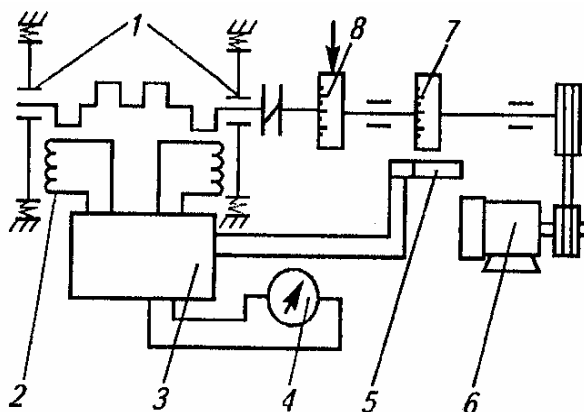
Схема станка для динамической балансировки деталей: 1 – опоры (люльки); 2 – датчик перемещений; 3 – блок усиления; 4 – миллиамперметр; 5 – лампа стробоскопа; 6 – электродвигатель; 7 – лимб стробоскопа; 8 – маховик
